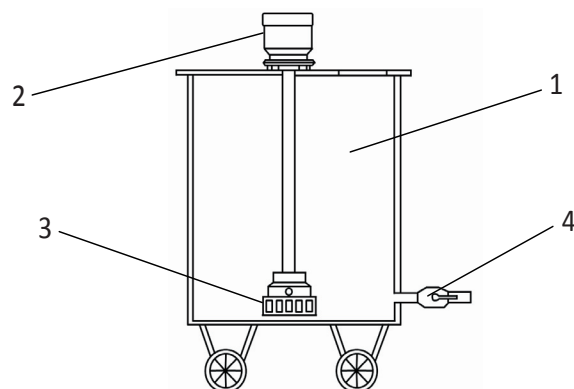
Схема агрегата для приготовления заменителей молока роторным диспергатором:
